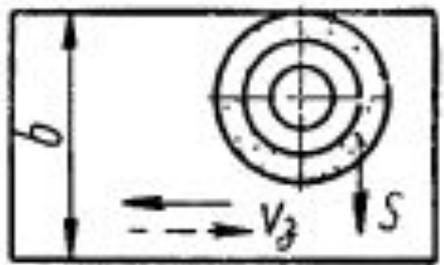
Схема обработки на плоскошлифовальных станках с обозначением движений:
